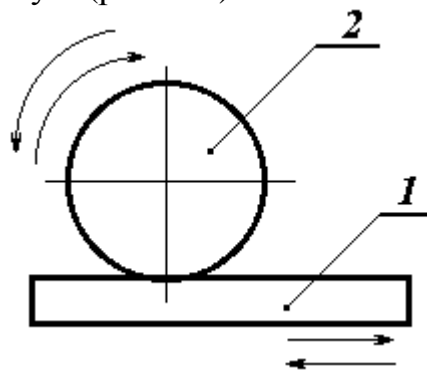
Реечная зубчатая передача: 1- зубчатое колесо; 2- рейка
